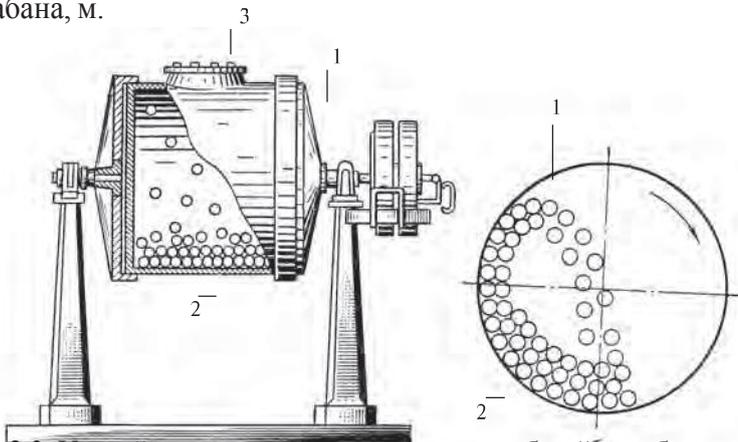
Устройство шаровой мельницы: а — общий вид; б — направление движения шаров; 1 — барабан; 2 — шары; 3 — загрузочный люк
